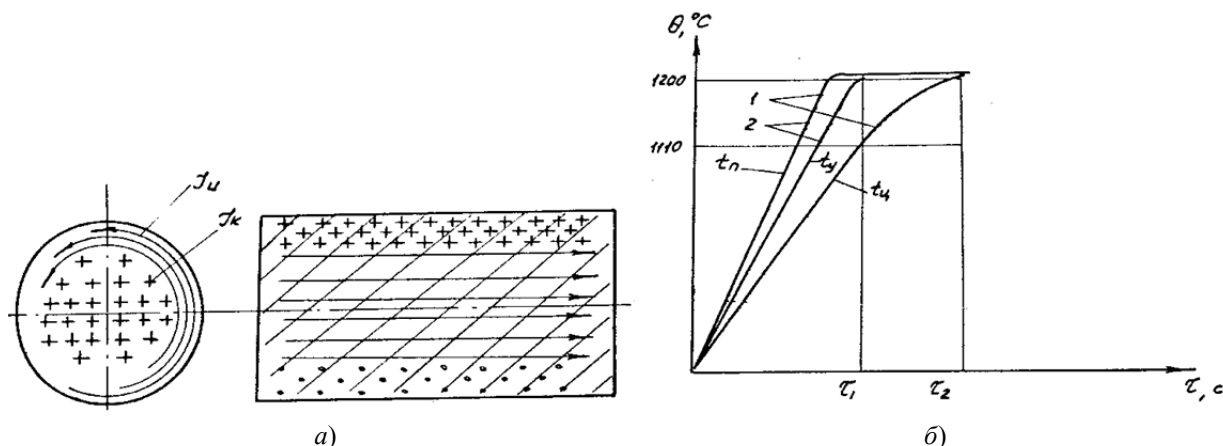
Схема скоростного нагрева заготовок перед штамповкой:
